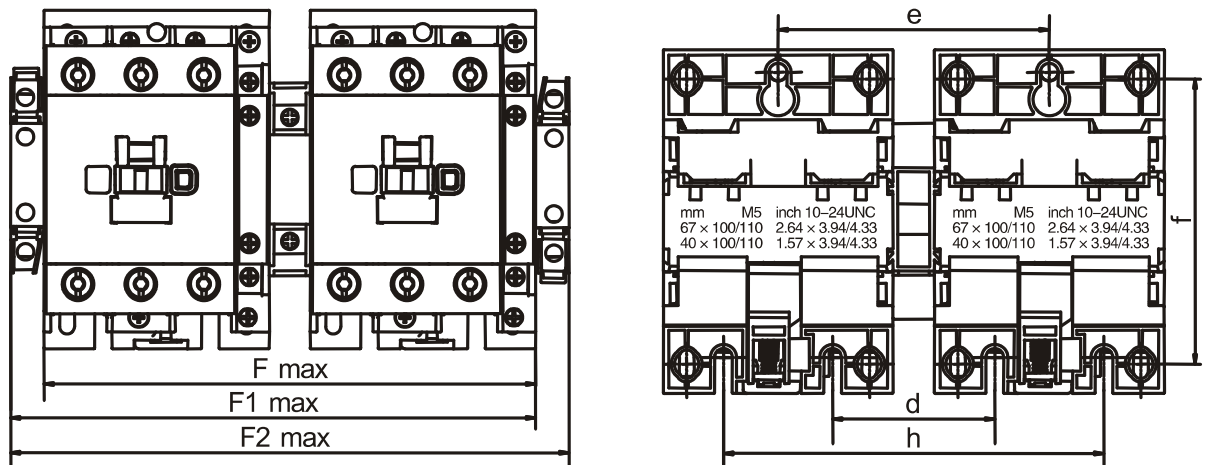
Габаритные и установочные размеры контакторов с реверсивной сборкой на токи 40-95А, мм.
